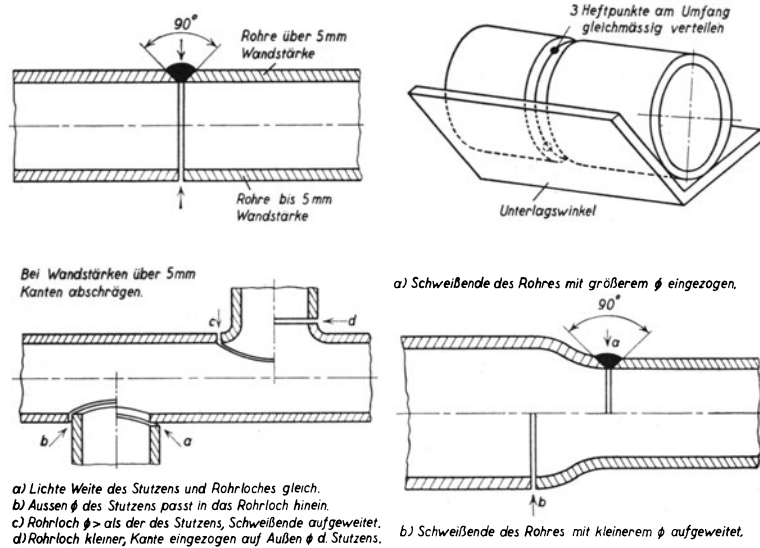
Rohrverbindungen durch Schweißen.
